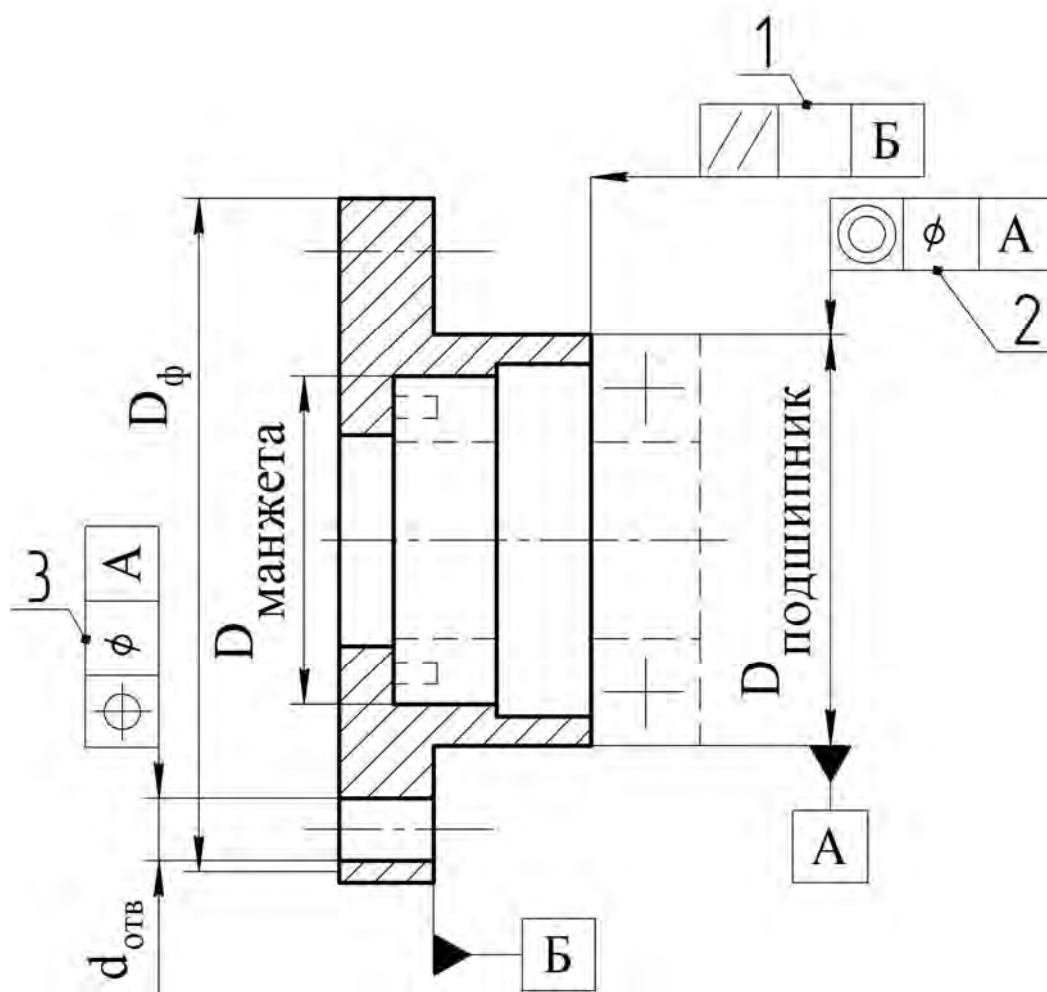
Допуски формы и расположения поверхностей крышки подшипника
